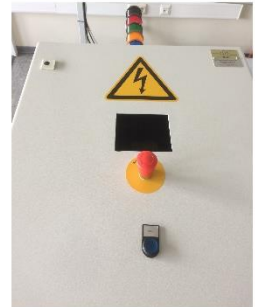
Montage und Installation der Maschine, Schaltschrank
